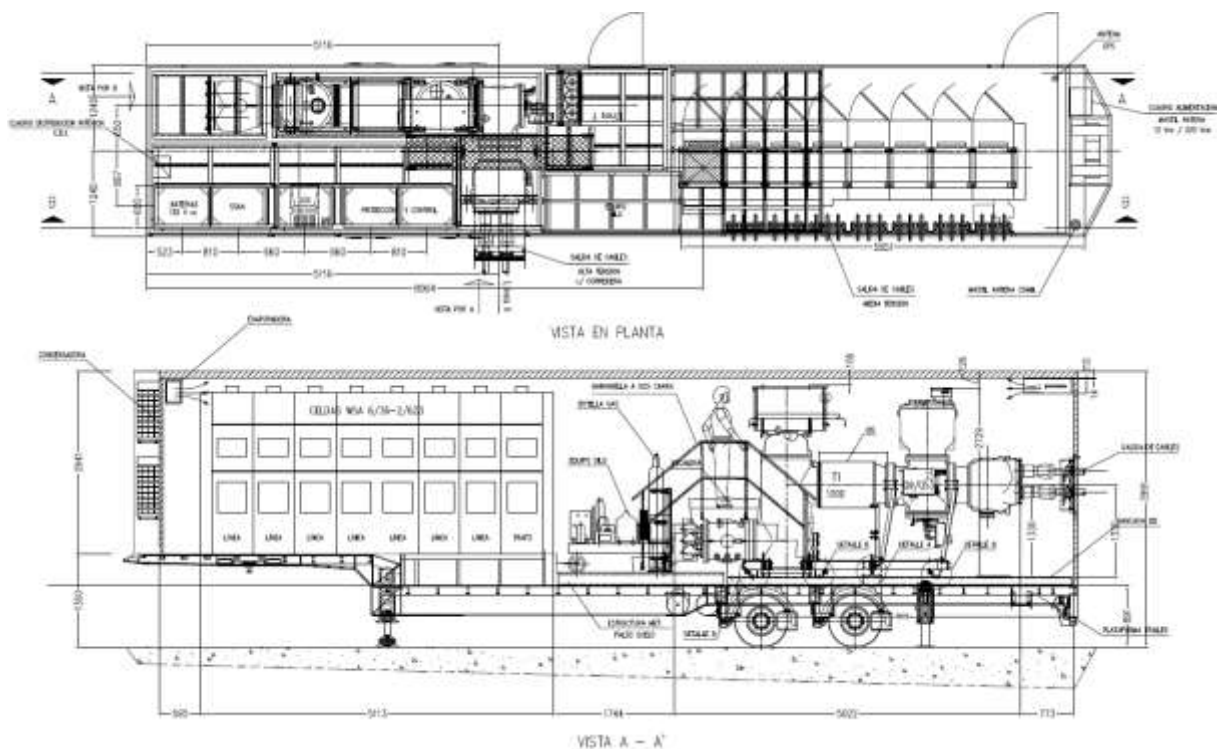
Vista en planta y Vista A-A' extraídas del plano 380.0007 –
